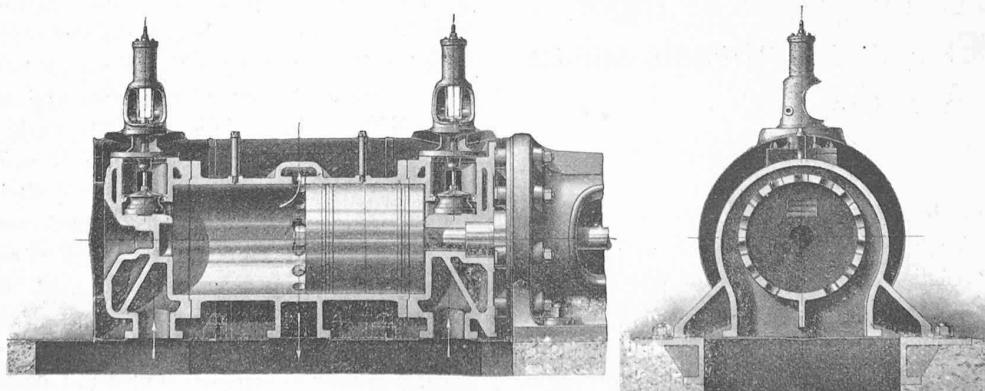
Coupes de la machine à vapeur Sulzer à flux continu.
